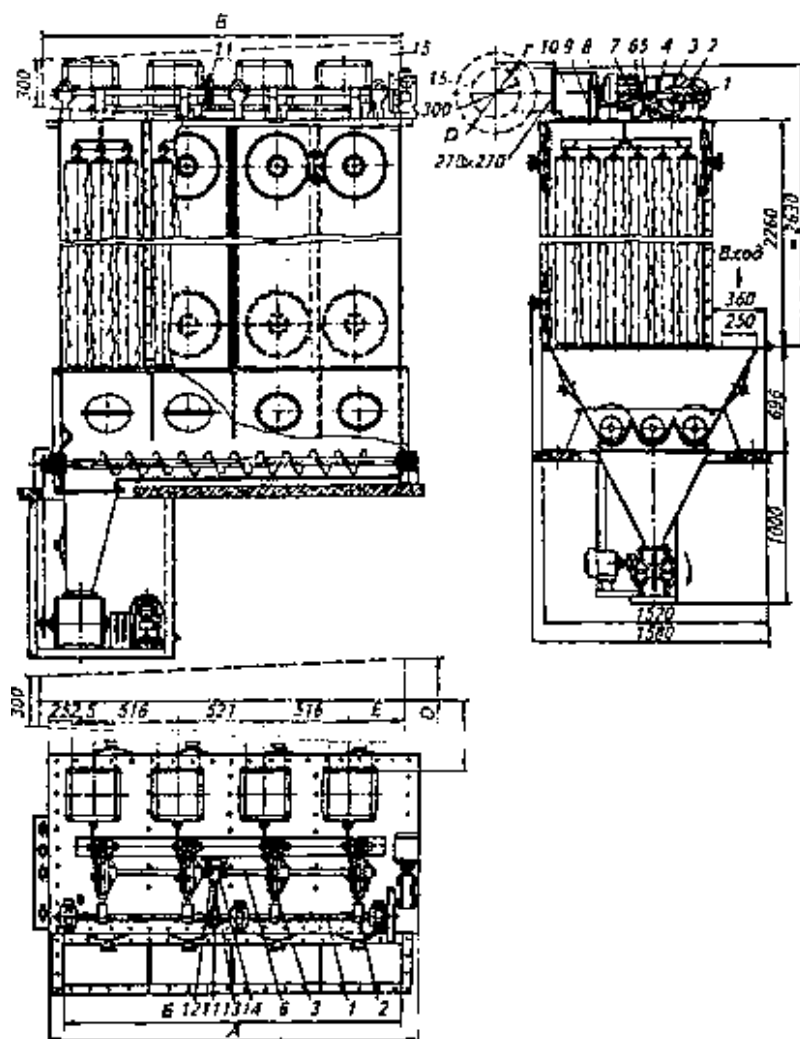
Всасывающий фильтр Г4-1БФМ: 1 – эксцентриковый вал; 2 – встряхивающий кулачок; 3 – рычаг; 4 – наклонный рычаг; 5 – кулачок; 6 – распределительный вал; 7 – тяга; 8 – продувочный клапан; 9 – рабочий клапан; 10 – выходная коробка; 11 – эксцентриковый механизм; 12 – храповое колесо с диском; 13 – шатун; 14 – рабочее храповое колесо; 15 – выходной коллектор
